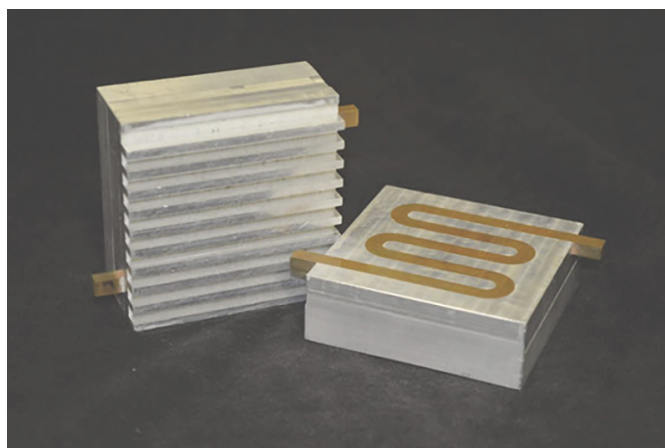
, Pieza de aluminio con geometría interna de cobre. Recuperada a partir de <https://3dprint.com/44405/fabrisonic-am-milling-process/>
